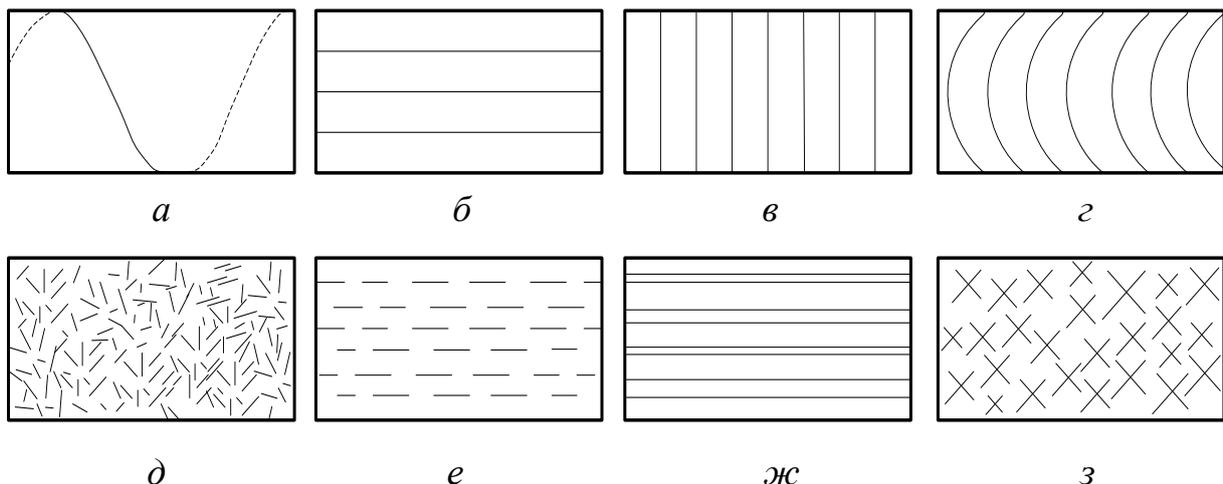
Расположение неровностей: а – точение, растачивание, сверление, зенкерование, развертывание; б – строгание; в – цилиндрическое резерование; г – торцовое фрезерование; д – доводка свободным абразивом; е – шлифование; ж – протягивание; з – суперфиниширование
